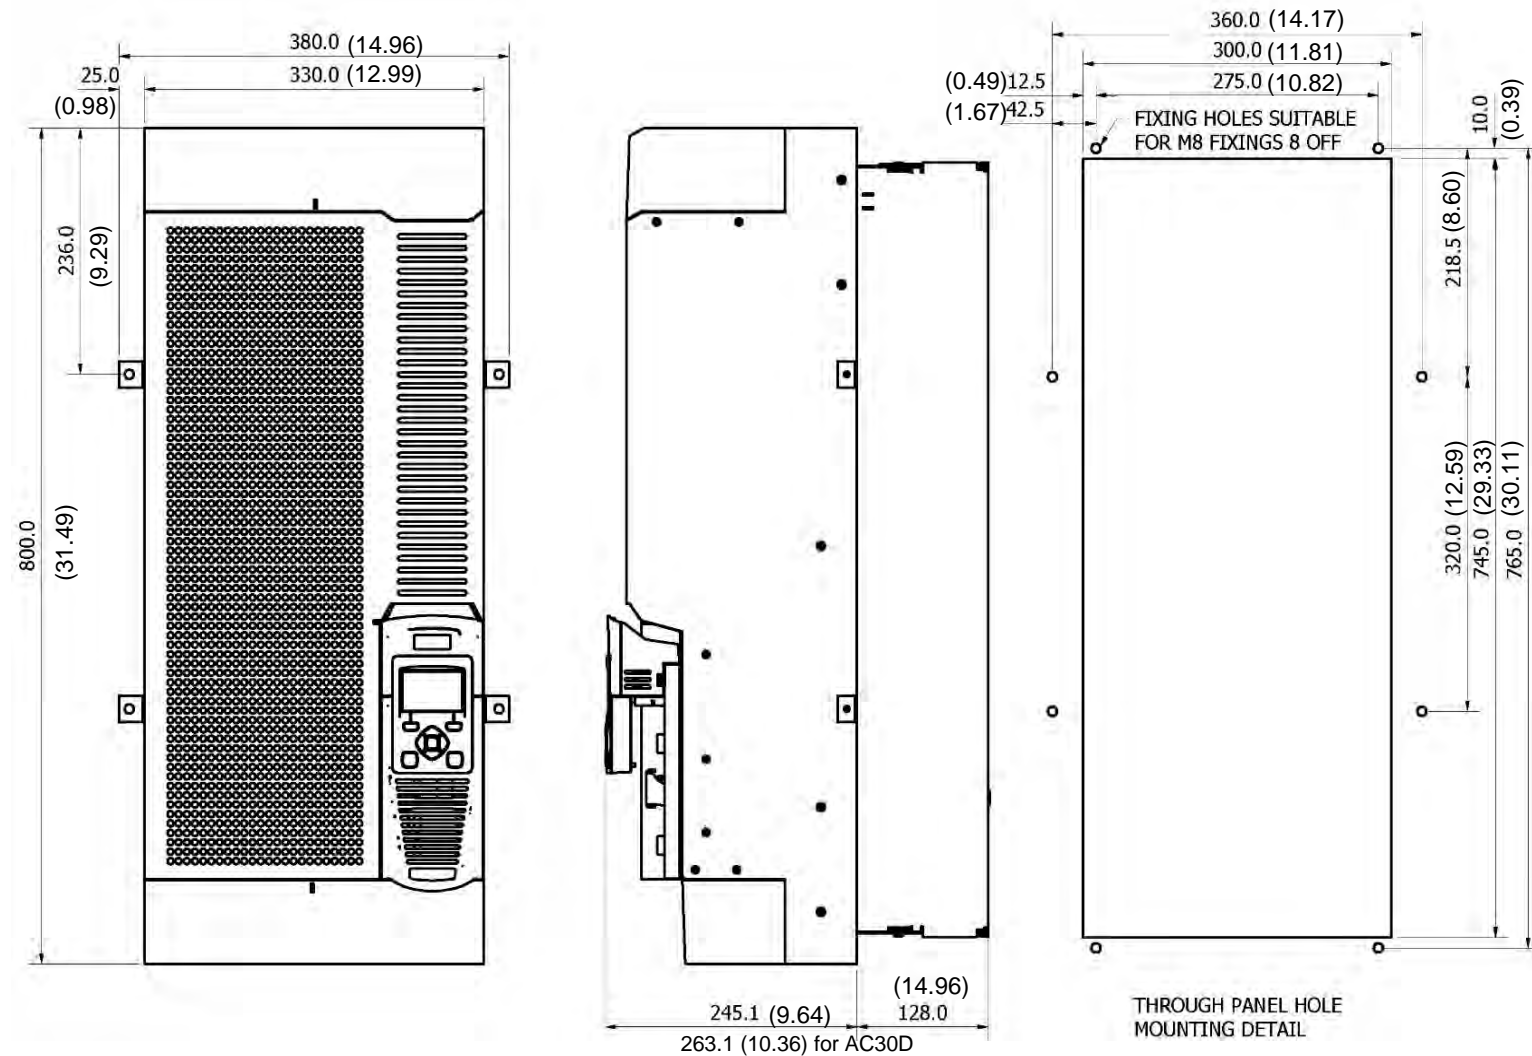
7 Dimensiones mecánicas de la unidad AC30V de montaje en panel - Tamaños J
